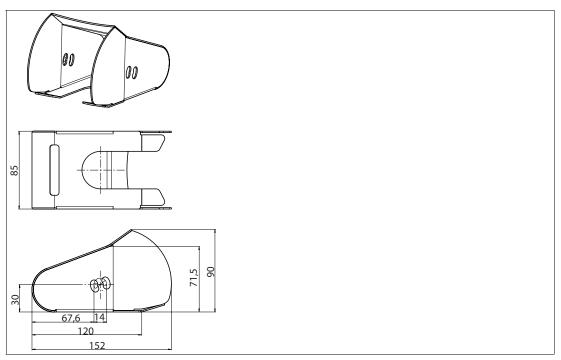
Abmessungen Halter für Barcode-Handheld
